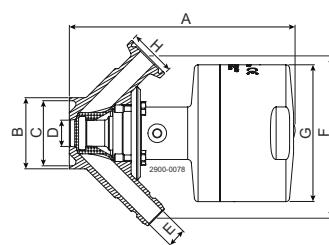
Pneumatique avec corps de vanne : Tuyau à collet à souder
